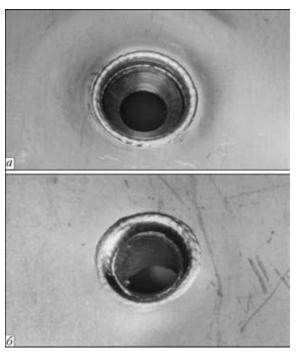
Внешний вид кольцевых швов при сварке отбортовка – тонкая пластина (×4) на штенгеле (a) и ниппеле (δ)
